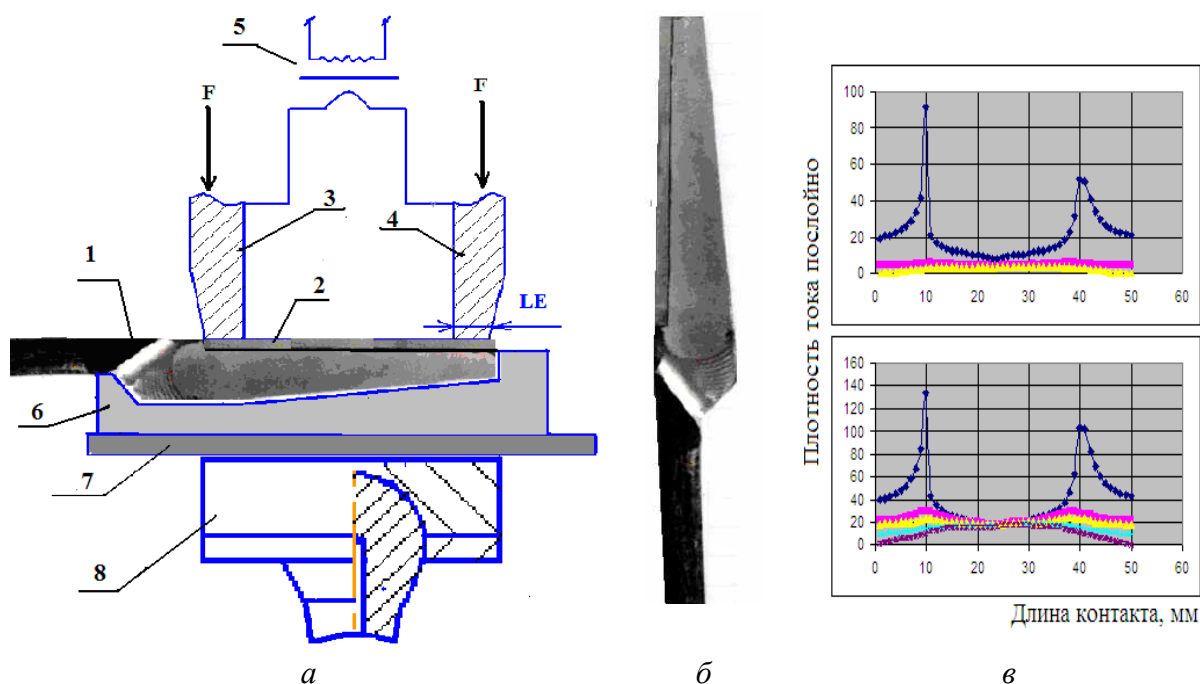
Наплавка твердого сплава на рабочую поверхность:
